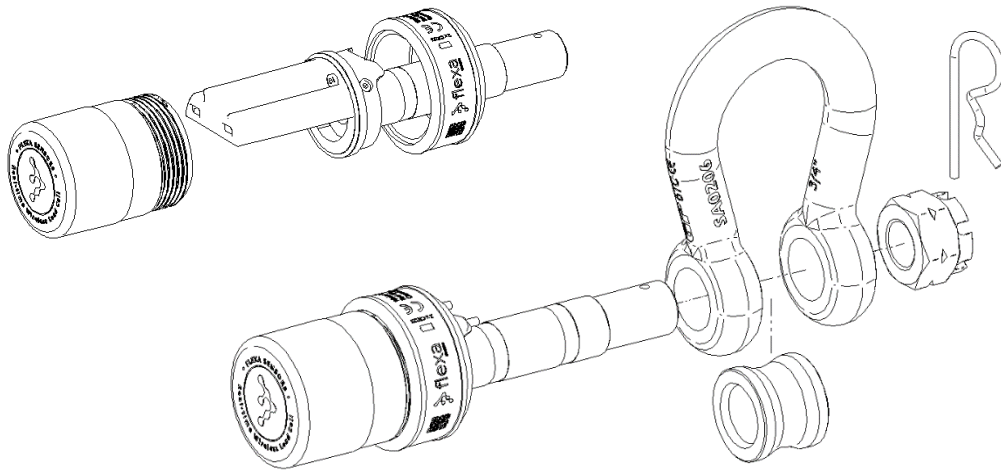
Cella di carico a grillo - Visione d'assemblaggio
